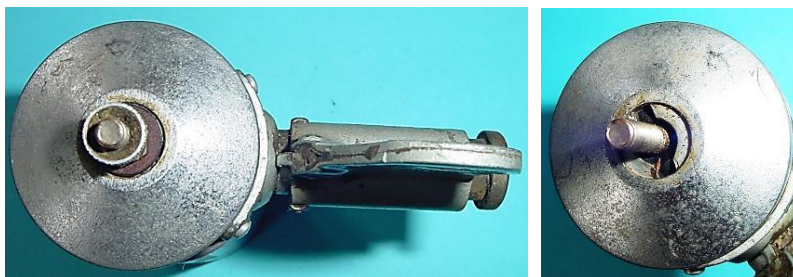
Bodenansicht mit und ohne Kabelanschlussmutter
